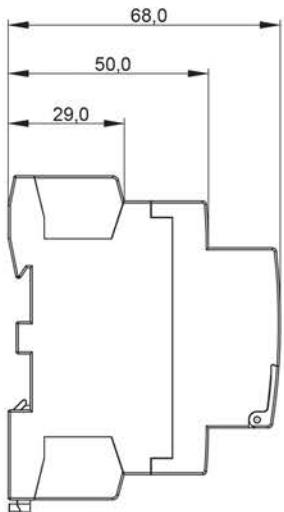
Габаритные размеры контакторов до 25 А, 4Р / Figure 2 – Overall dimensions of contactors up to 25 A, 4P
